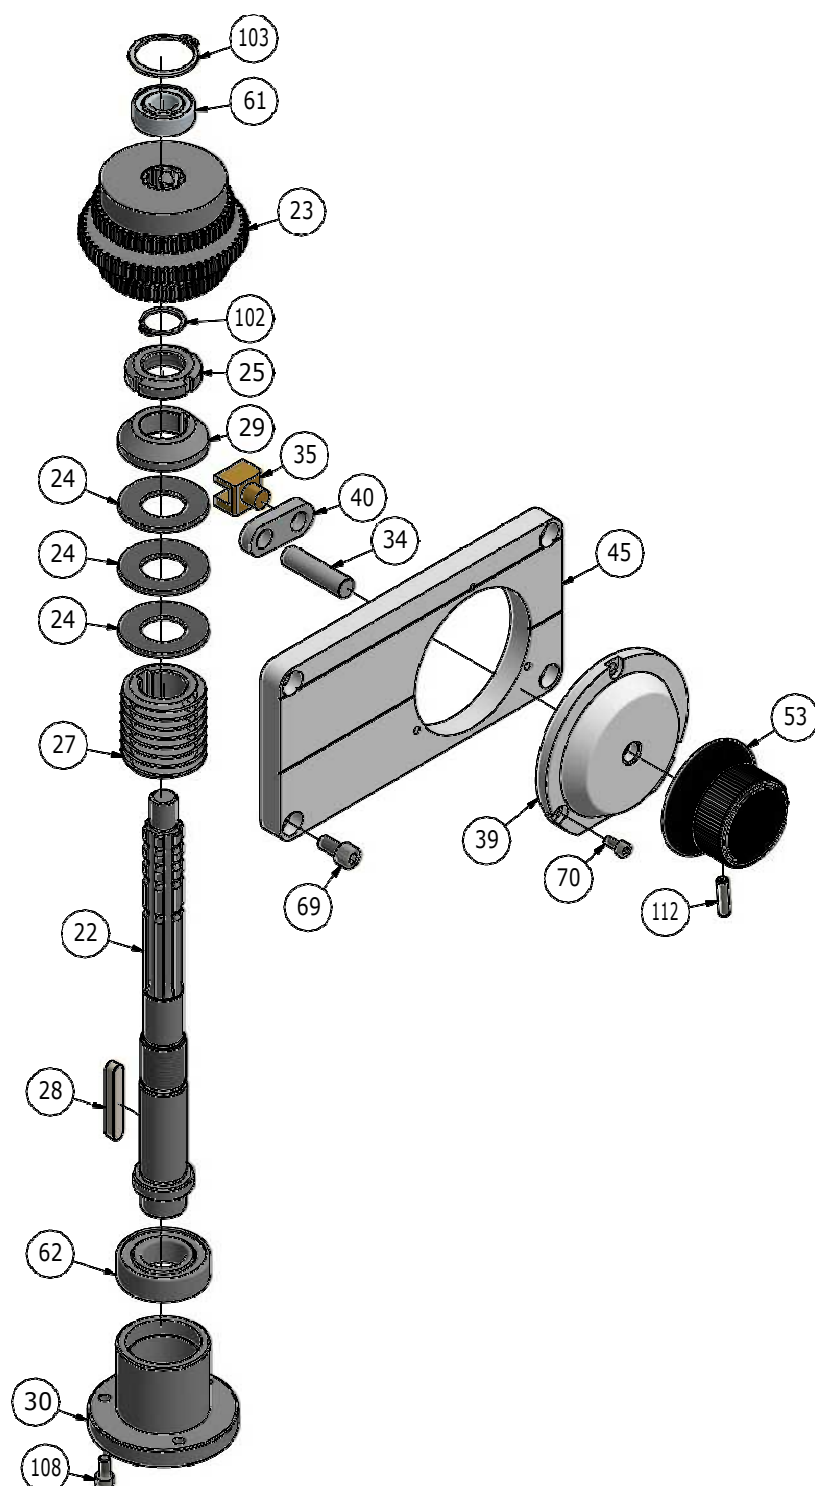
GetriebeTeilB - Elemento de engranaje B
